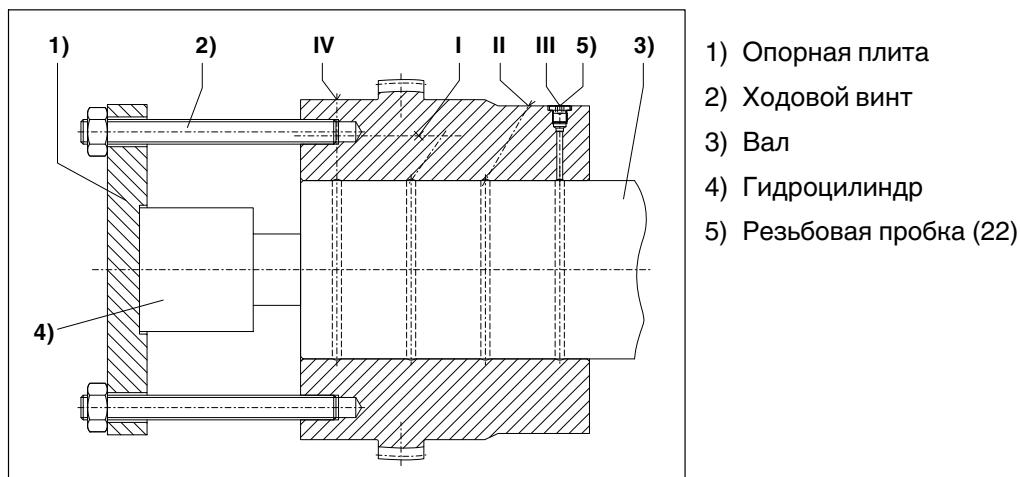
Демонтаж муфтовых частей (1/2) при цилиндрической прессовой связи
